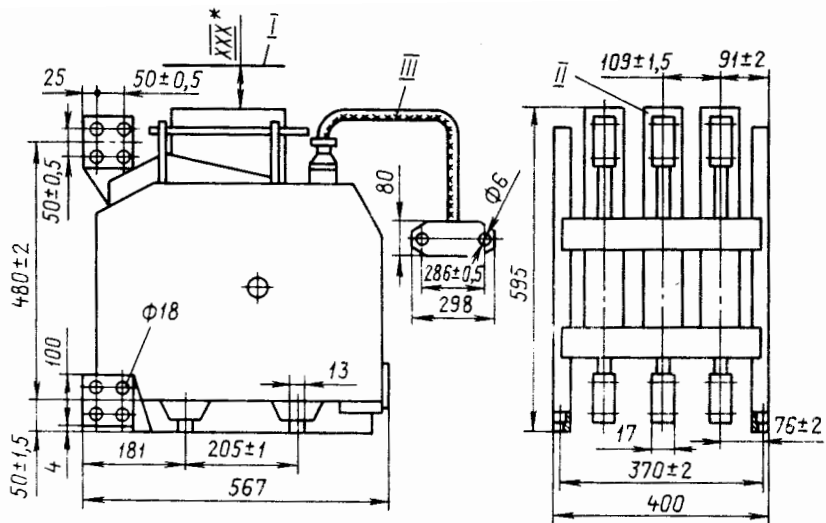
Габаритные и установочные размеры выключателей 3250 в двух- и трехполюсном исполнении:
